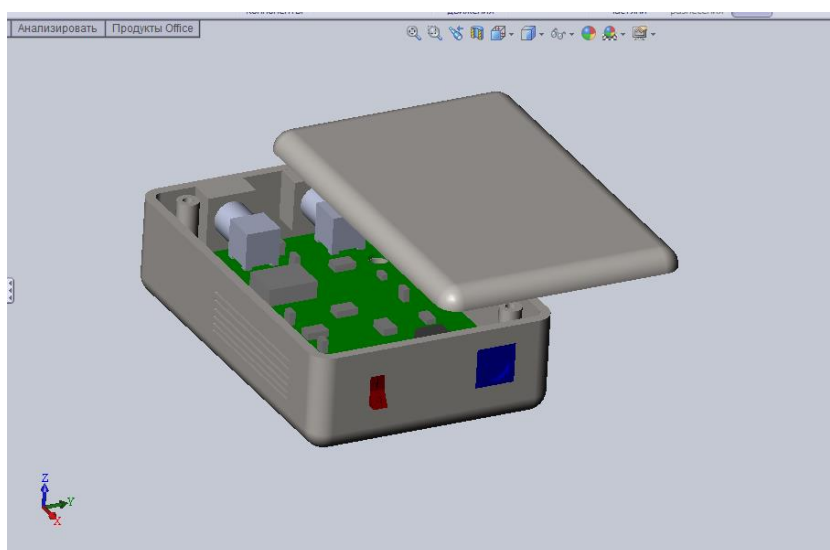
(б). Конструкция деталей и сборок «Преобразователя напряжения»
